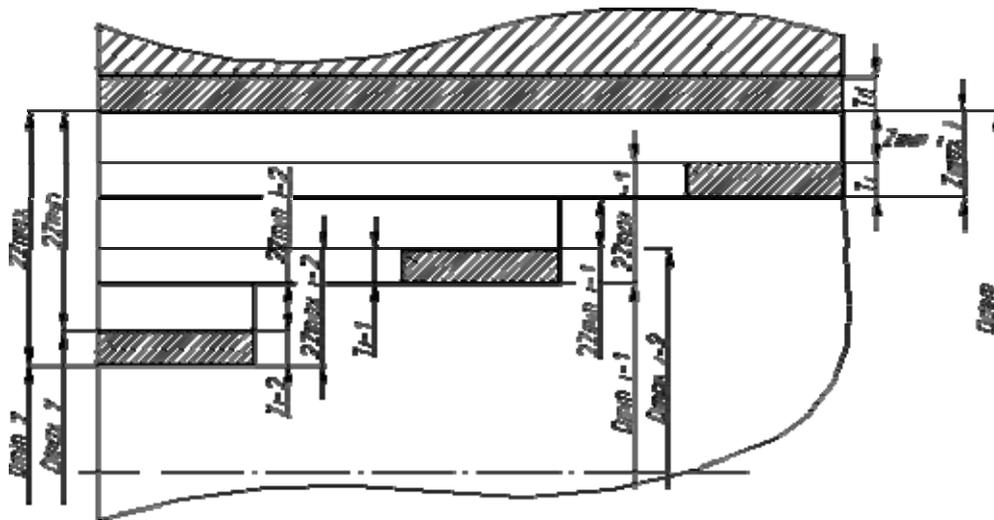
Схема связей между межпереходными размерами, припусками и допусками для охватывающих поверхностей
